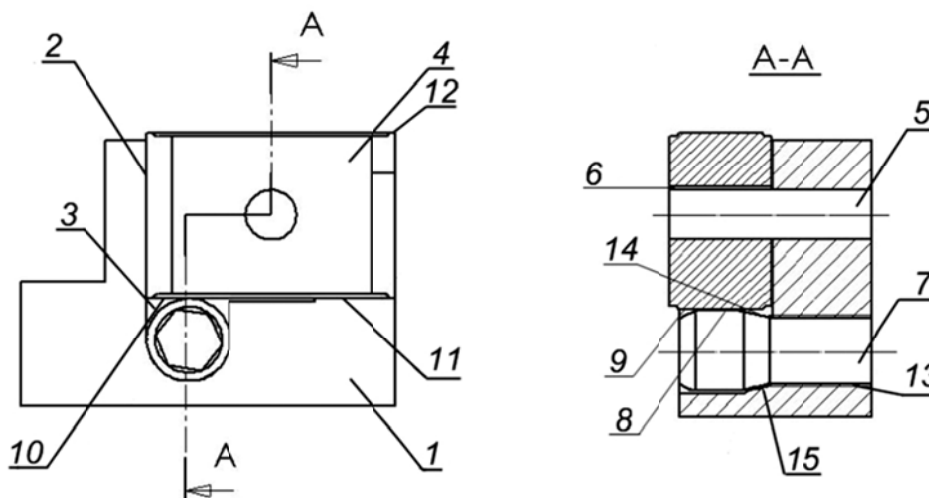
Усовершенствованная конструкция сборного резца с тангенциальным креплением пластины (патент № 45677)
